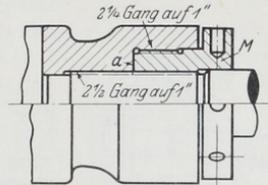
Befestigung der Stange durch Differentialgewinde.
